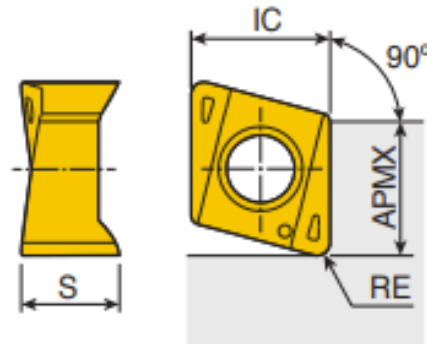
Фреза 4N TE90-212-12-04
